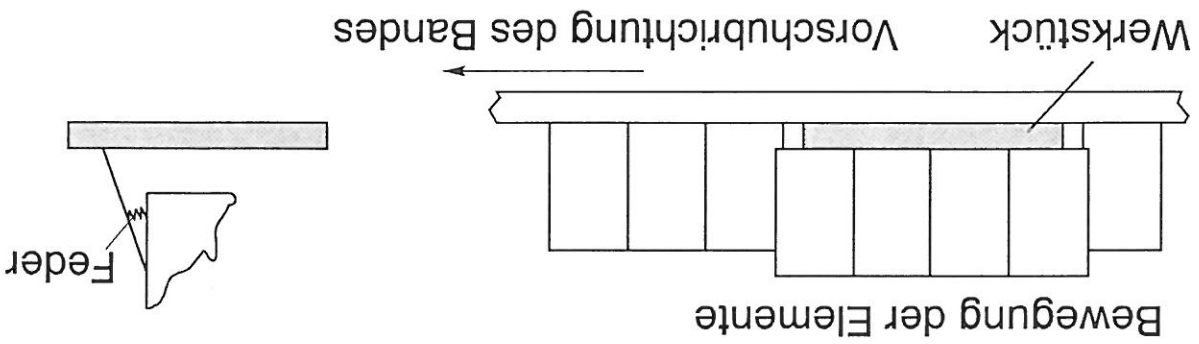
Federbetätigte Rechteckelemente
